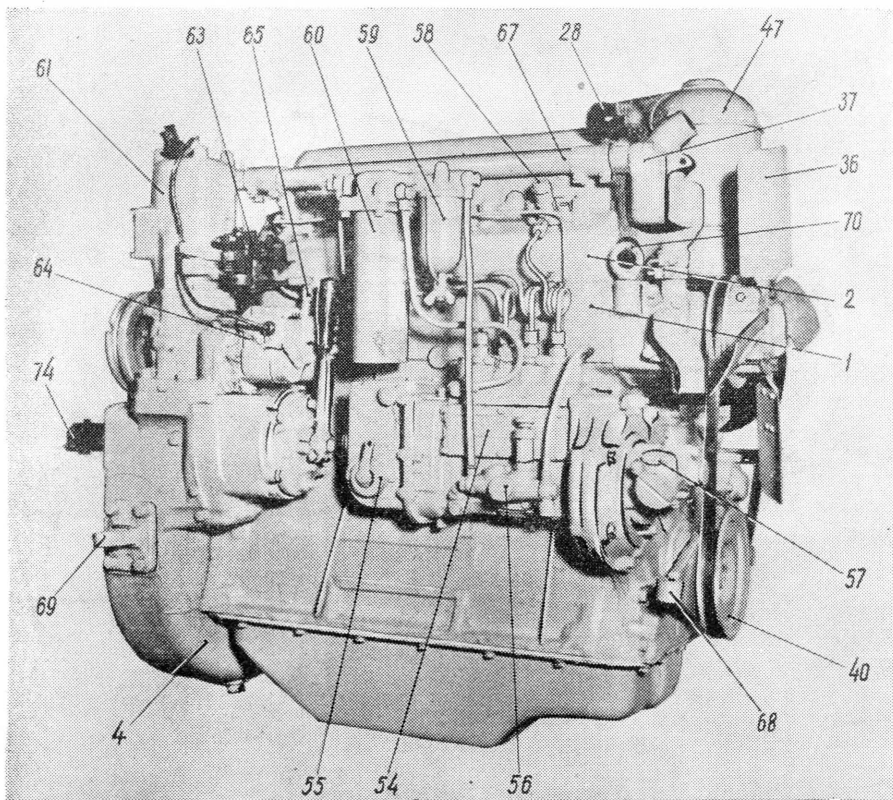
Двигатель Д-48Т (вид со стороны топливной аппаратуры)
